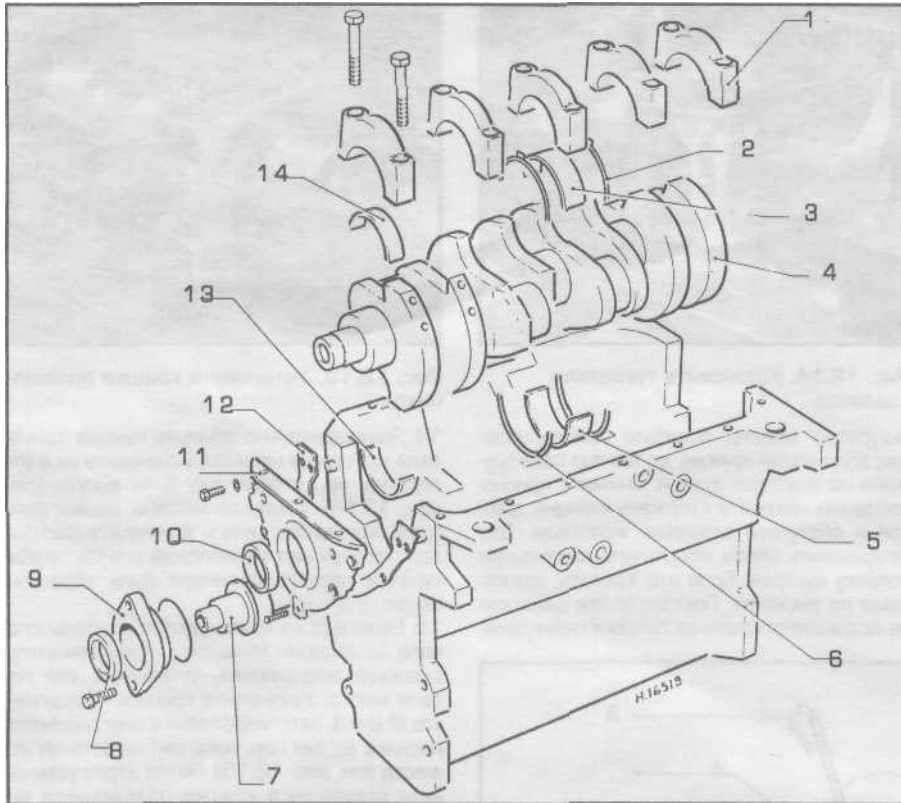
Детали блока цилиндров и коленчатого вала
